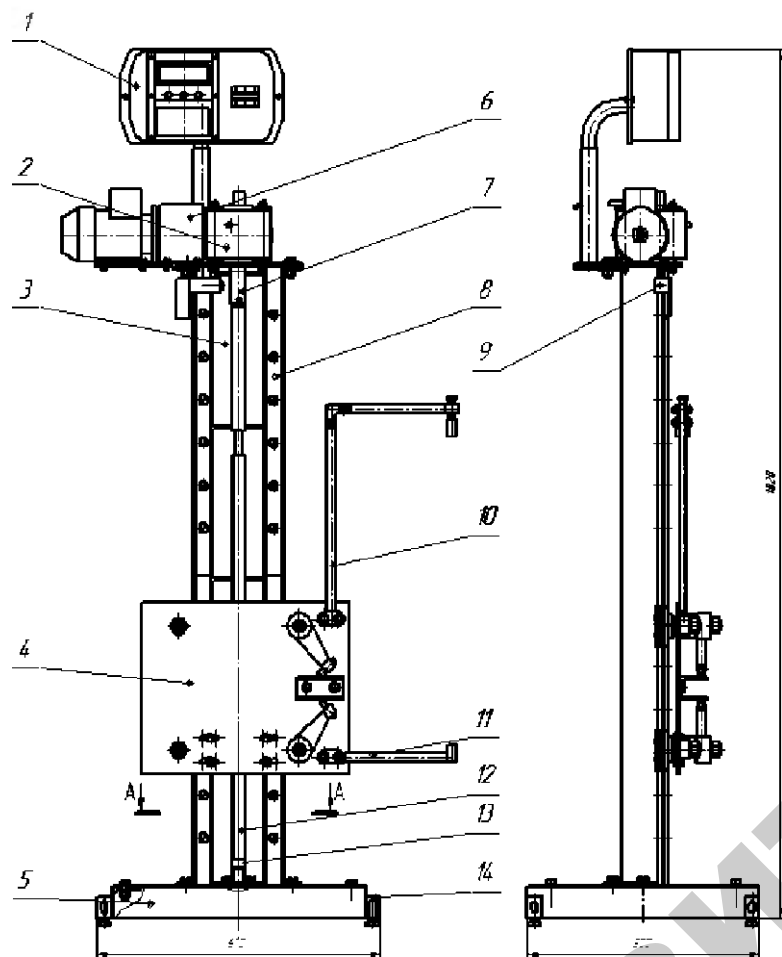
Общий вид установки для вертикального перемещения заготовки:
